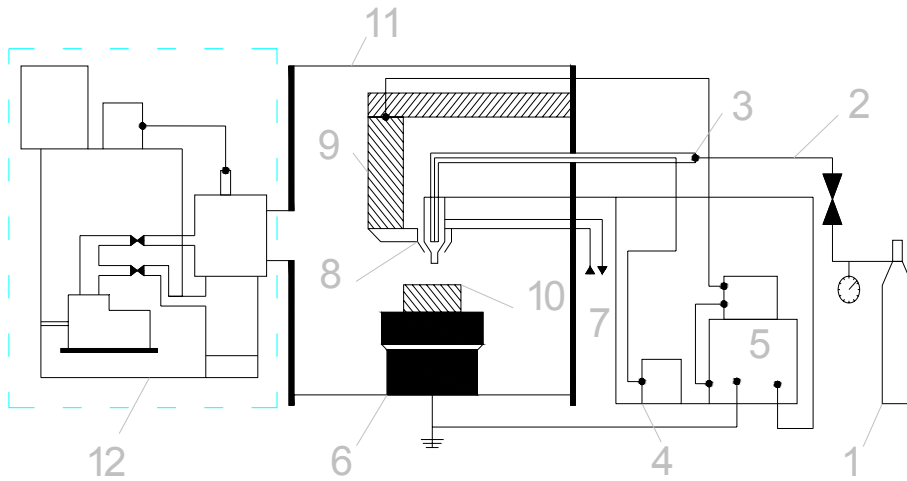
Принципиальная схема установки для сварки горячим полым катодом в вакууме:
